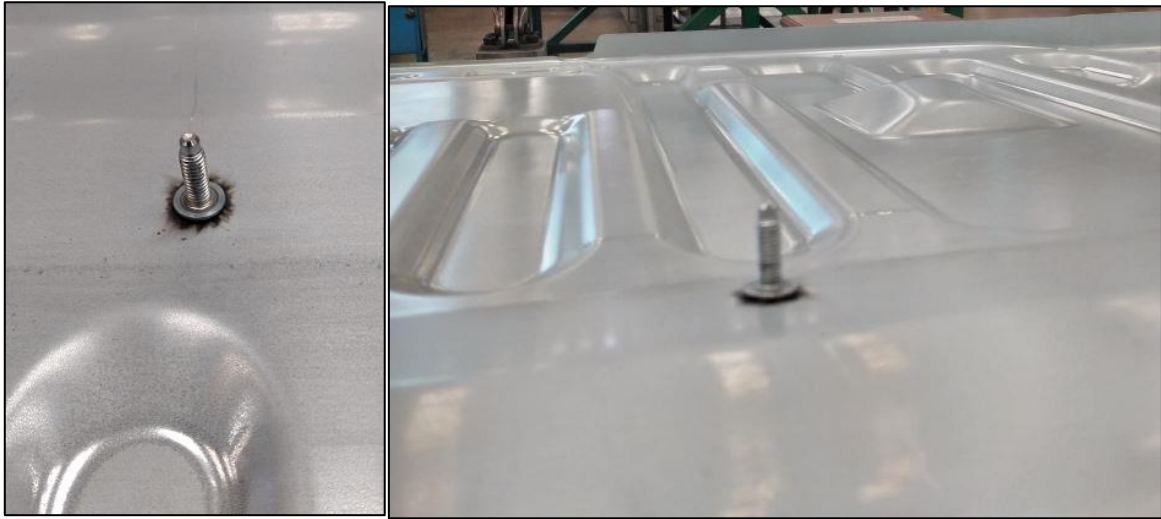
Vista frontal y lateral del tornillo soldado por proyección.
